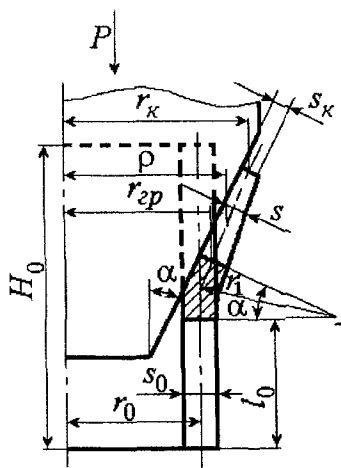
Схема раздачи трубной заготовки коническим пуансоном
